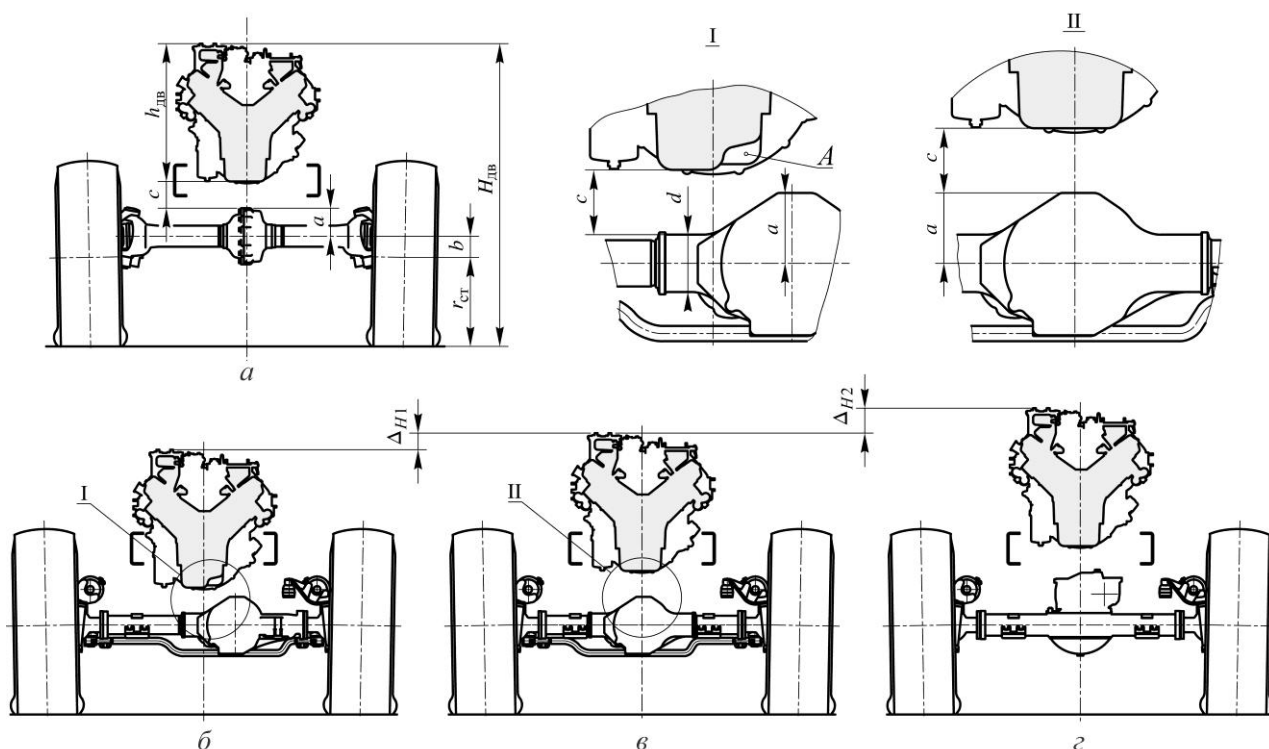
Влияние высоты центрального редуктора главной передачи на расположение двигателя:
